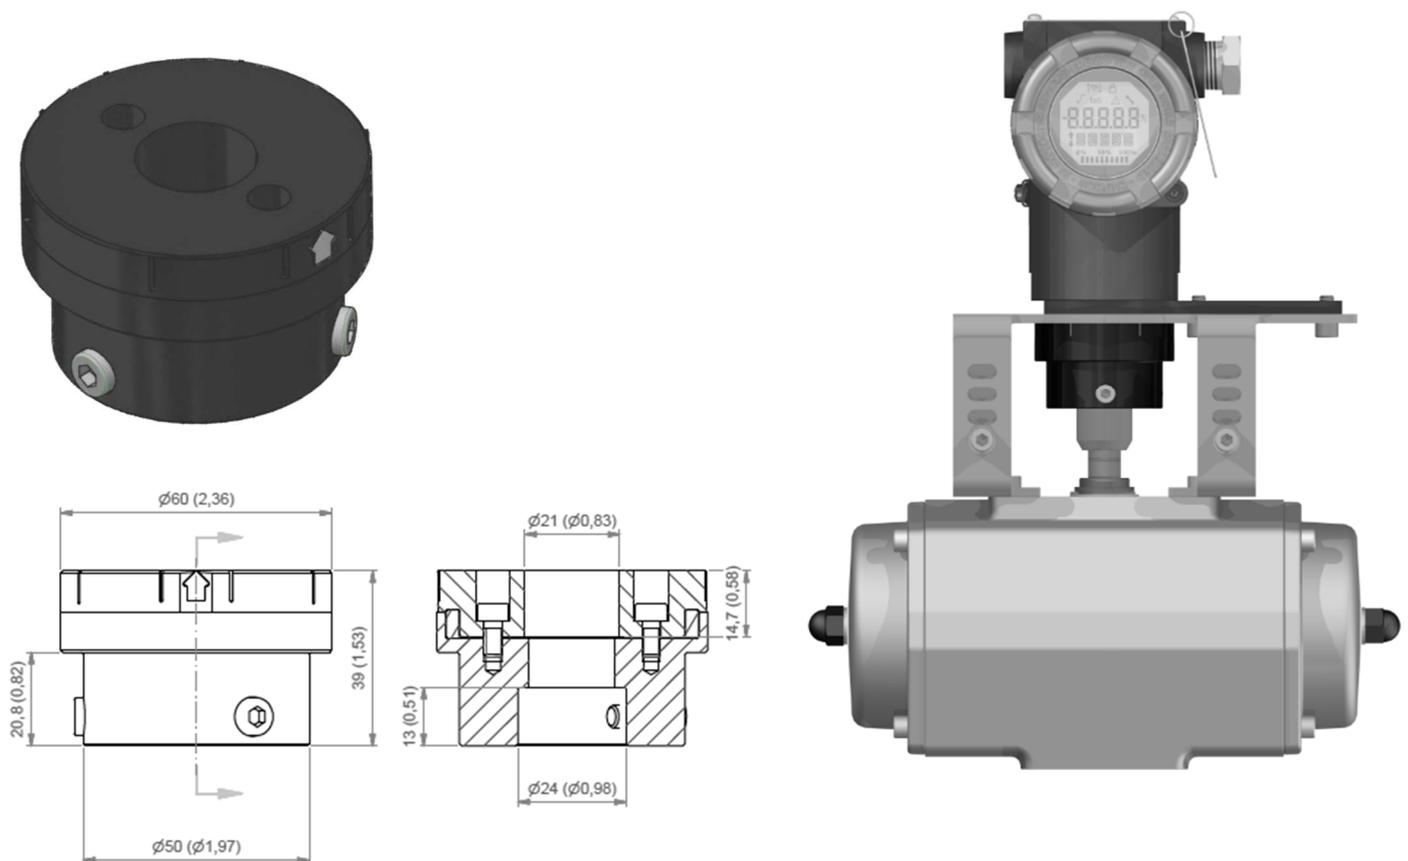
Dimensiones y montaje del imán giratorio.
